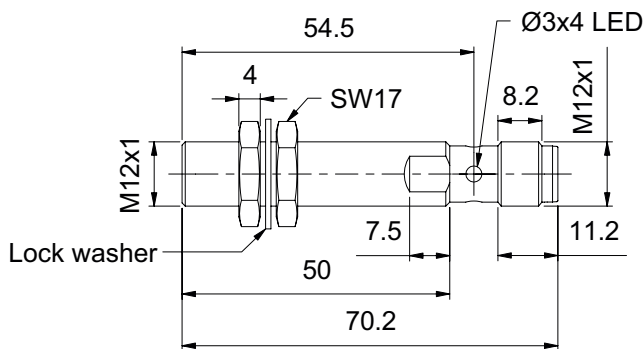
Lange Ausführung, bündiger Einbau, Steckversion
